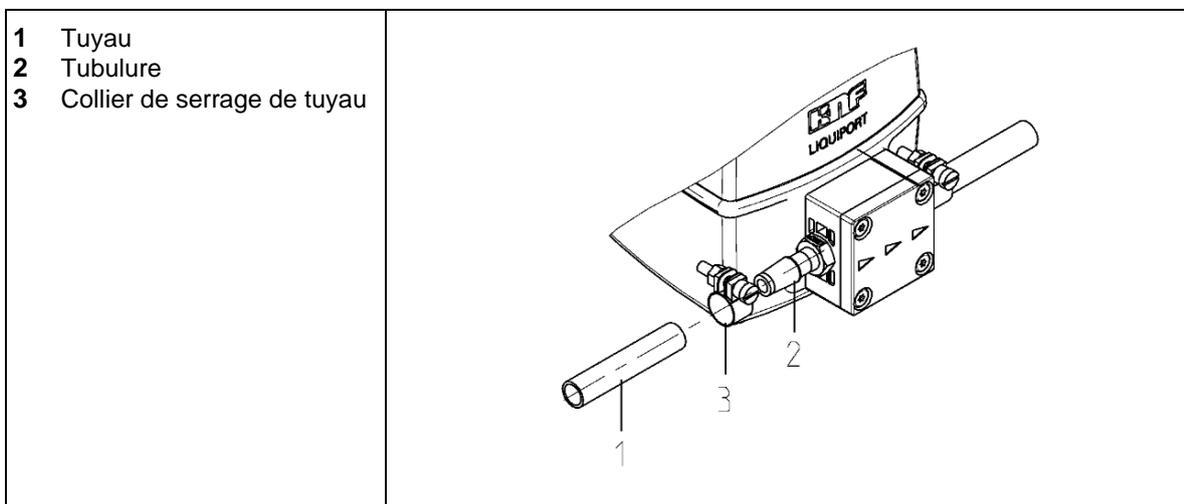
Tubulure DI 8 mm ou DI 12 mm
